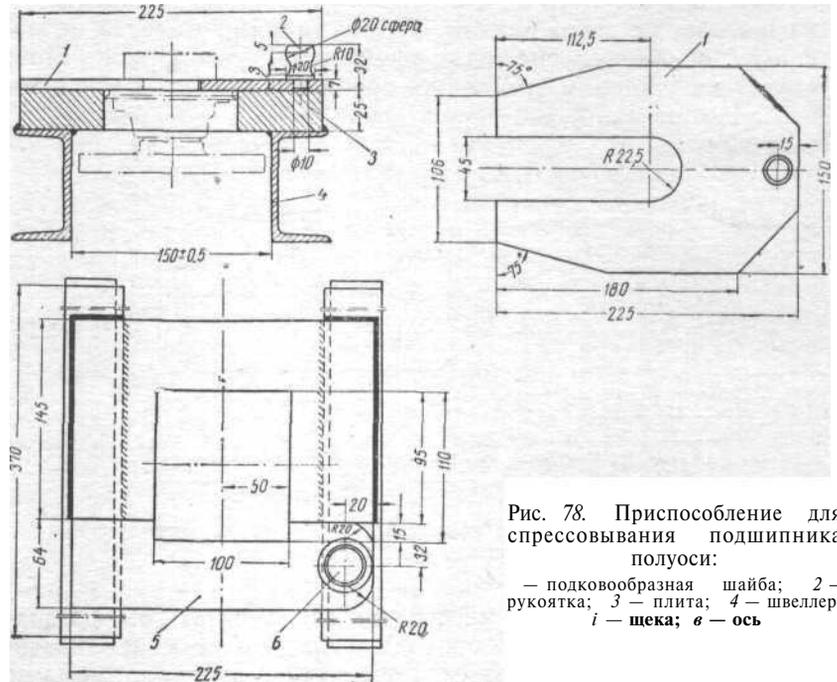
Приспособление для спрессовывания подшипника полуоси:
